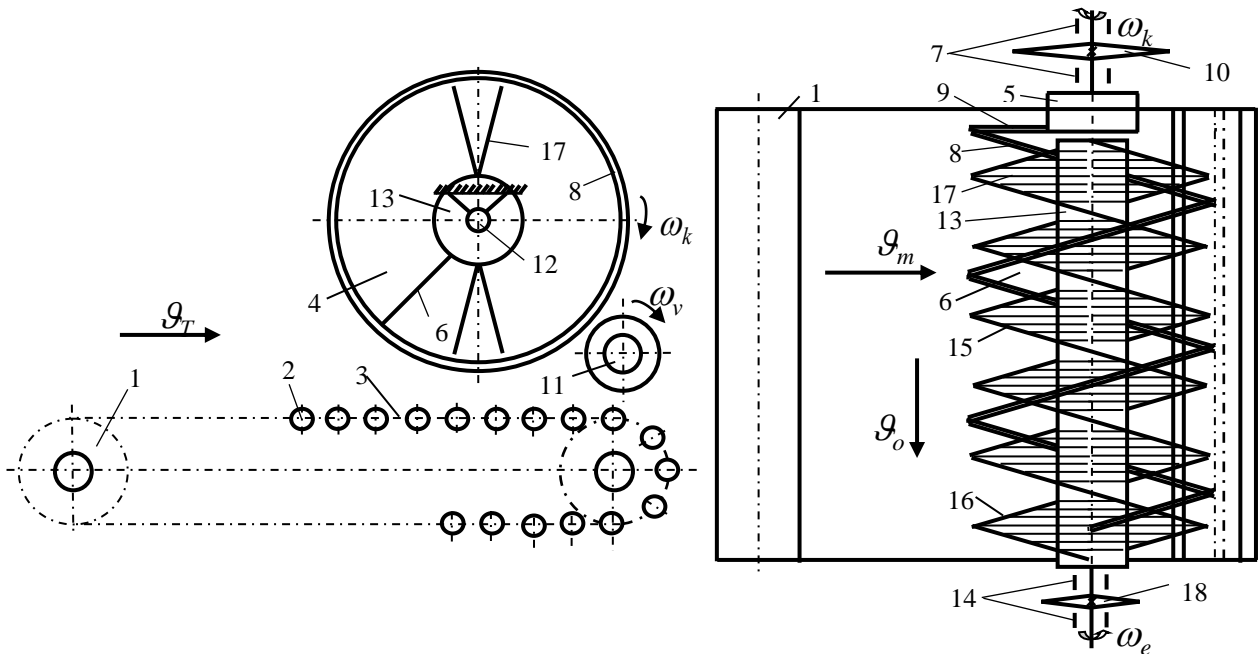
Конструктивна схема очисника вороху: 1 – подавальний транспортер; 2 – пруток; 3 – робоча гілка; 4 – комбінований робочий орган; 5 – пустотілий гвинтовий циліндр; 6 – виток; 7, 14 – опора; 8 – труба; 9 – фланець; 10, 18 – зірочка; 11 – відкидний валець; 12 – приводний вал; 13 – барабан; 15, 16 – гвинтова лінія; 17 – очисні елементи.
